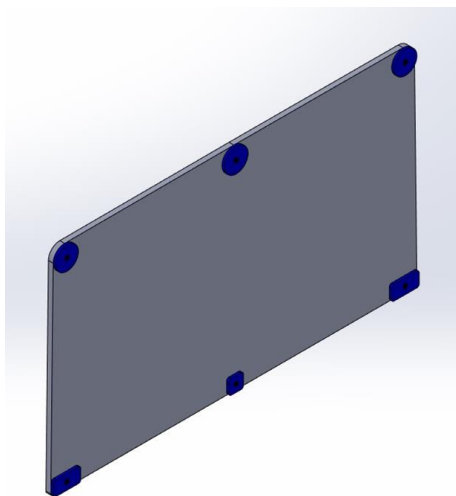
Conjunto Placa Frontal e Patelas a Soldar no Quadro
